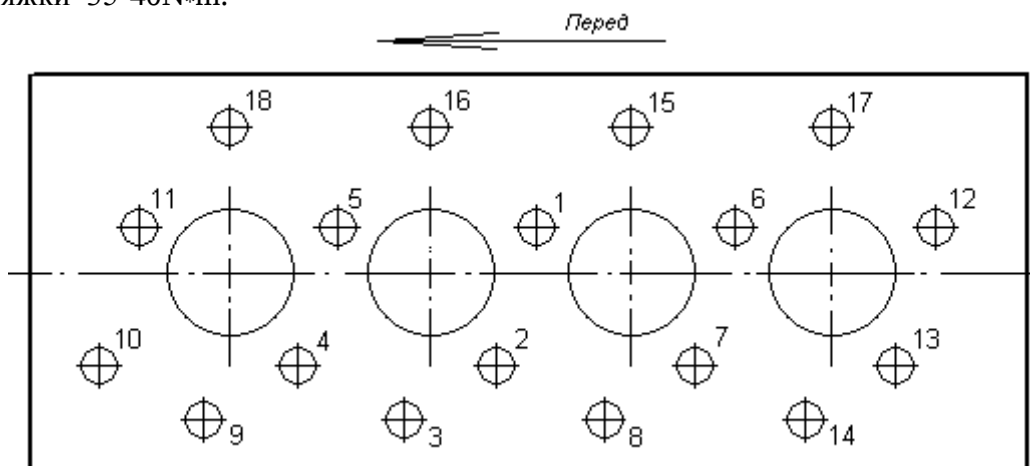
Порядок подтяжки гаек головки блока цилиндров
